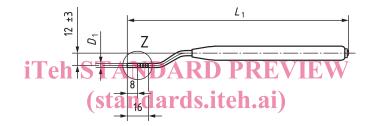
Type 1, Forme B: Sinutome, à extrémité déportée
